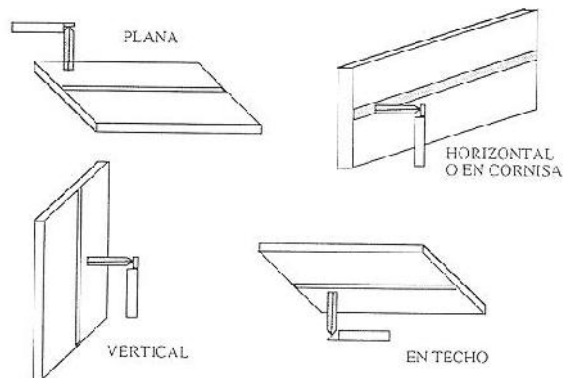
3: Posición de soldadura en placa de soldadura de ranura
